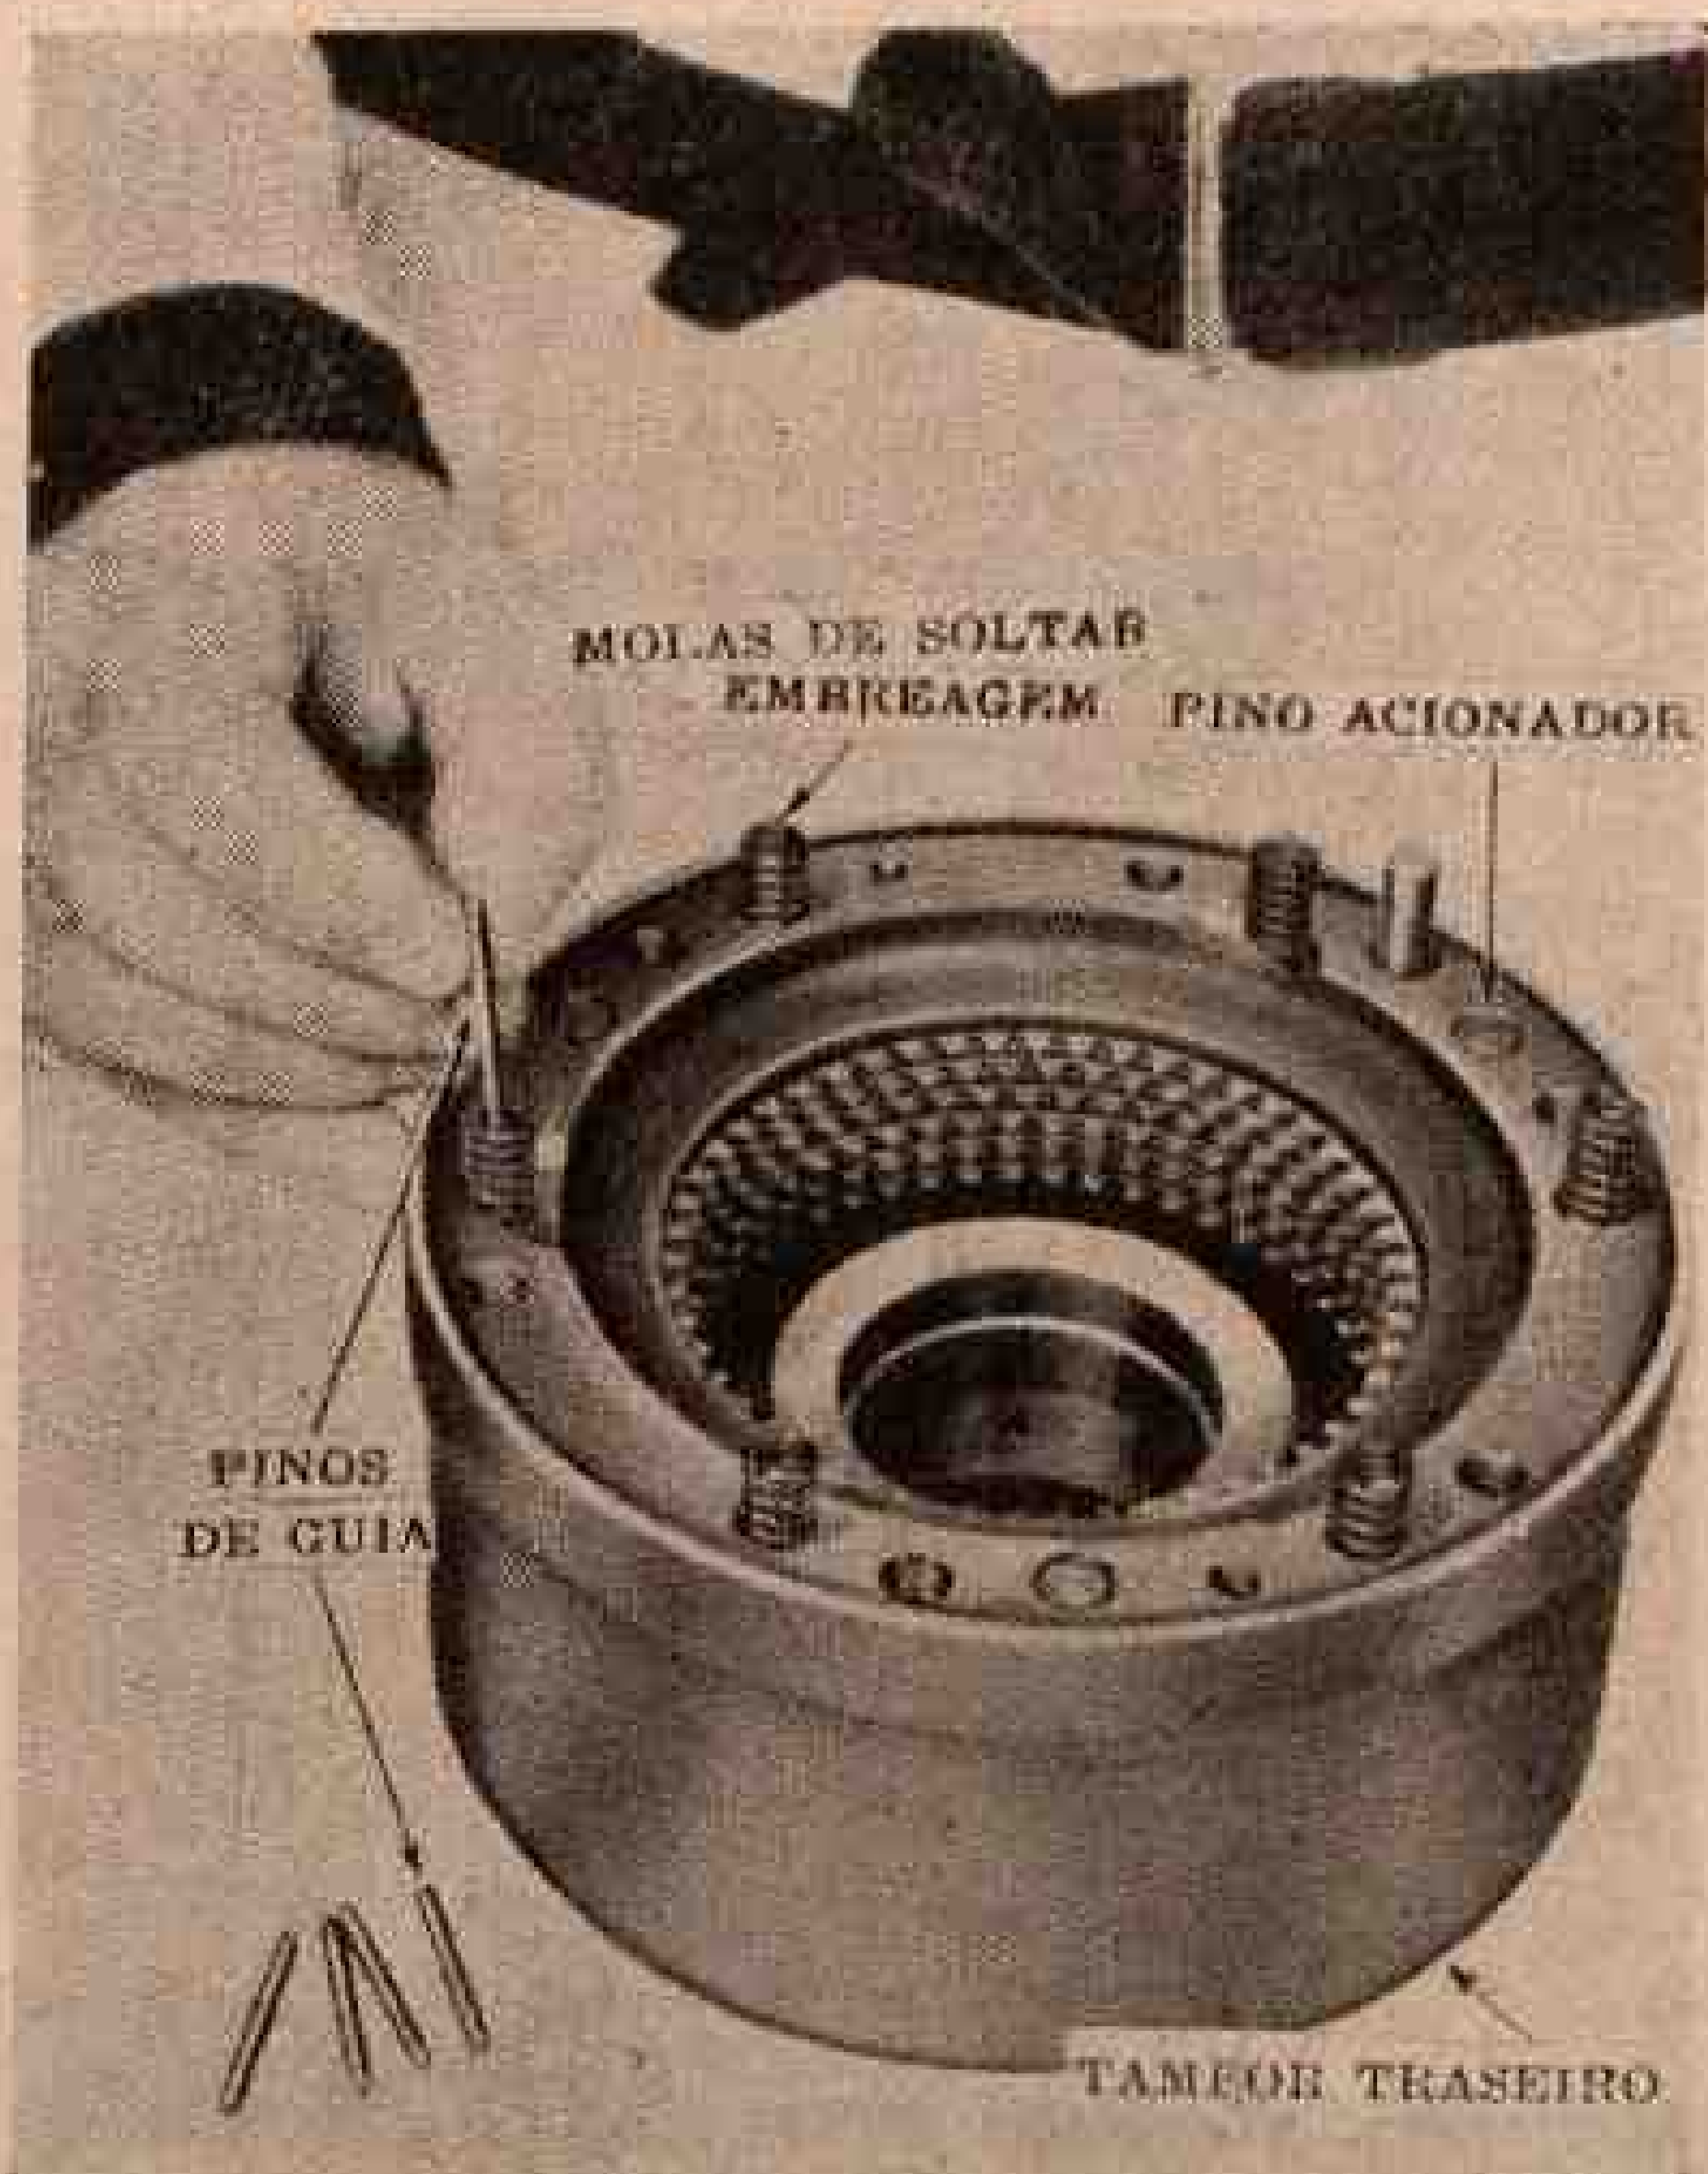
Instalando a mola de soltar embreagem e os pinos da guia.
